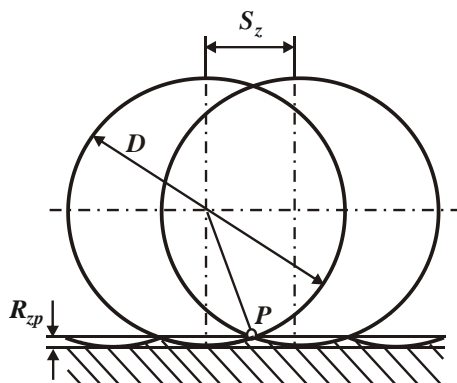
Расчетный микропрофиль обработанной поверхности при фрезеровании цилиндрической фрезой [1]
